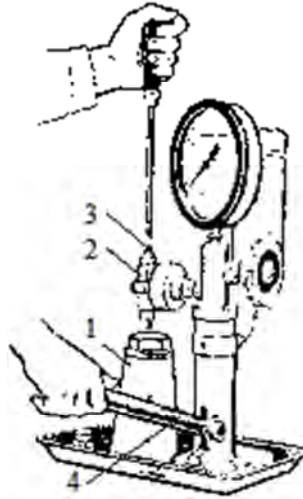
Регулировка форсунки на приборе КИ-1609А:
